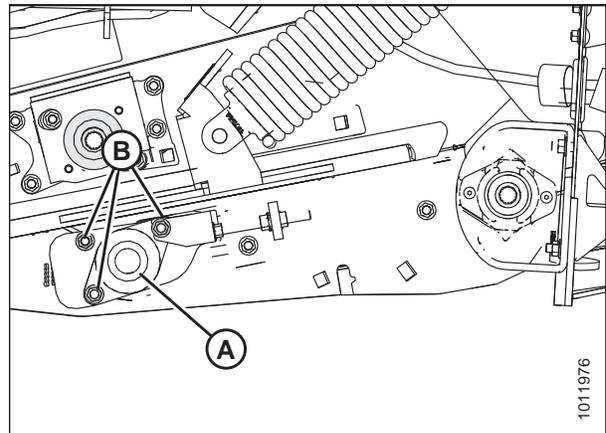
Rodillo tensor de la cama frontal del lado izquierdo
